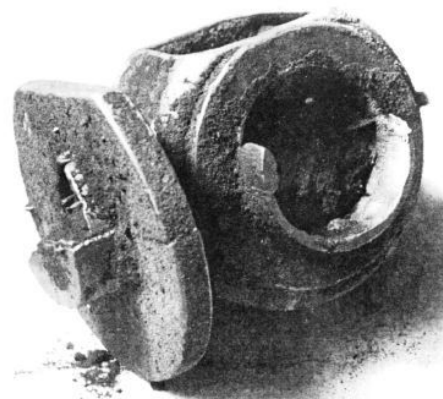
Отливка «Корпус вентиля» с дефектом «Недолив»
